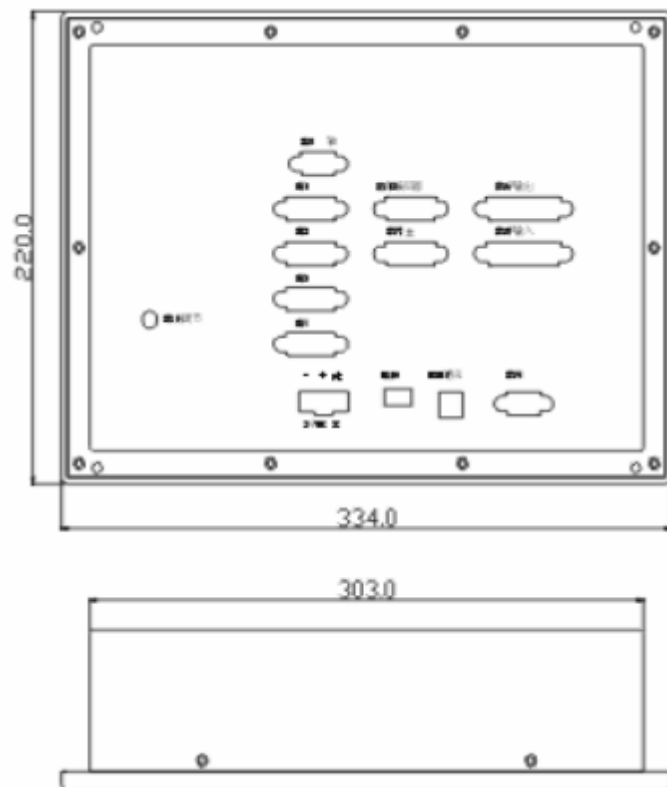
Dimensiones generales del controlador ADTECH CNC 4620
